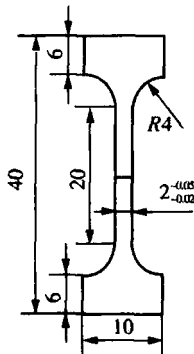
焊接接头的原位拉伸试样 (安装位置)
